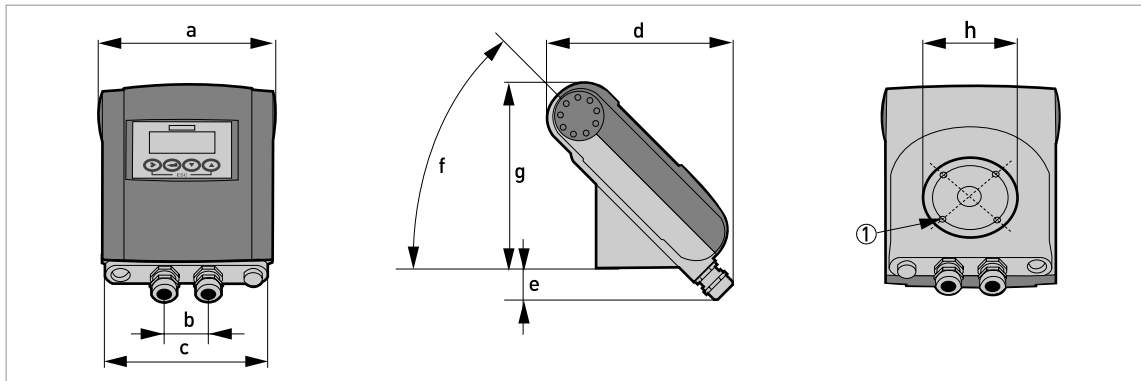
Abmessungen für Kompaktausführung (45°), Aluminiumgehäuse
